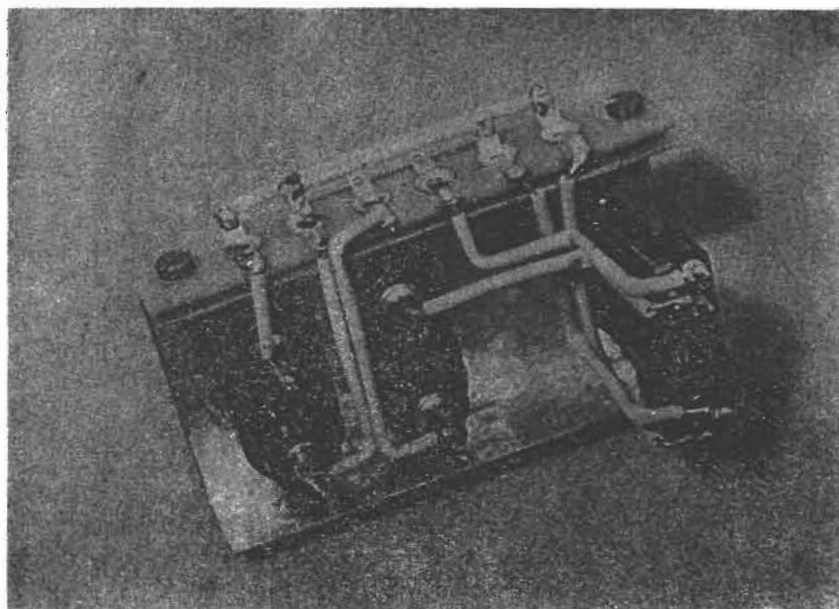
Prospetto del pezzo dei collegamenti con le prese B1...B4.
